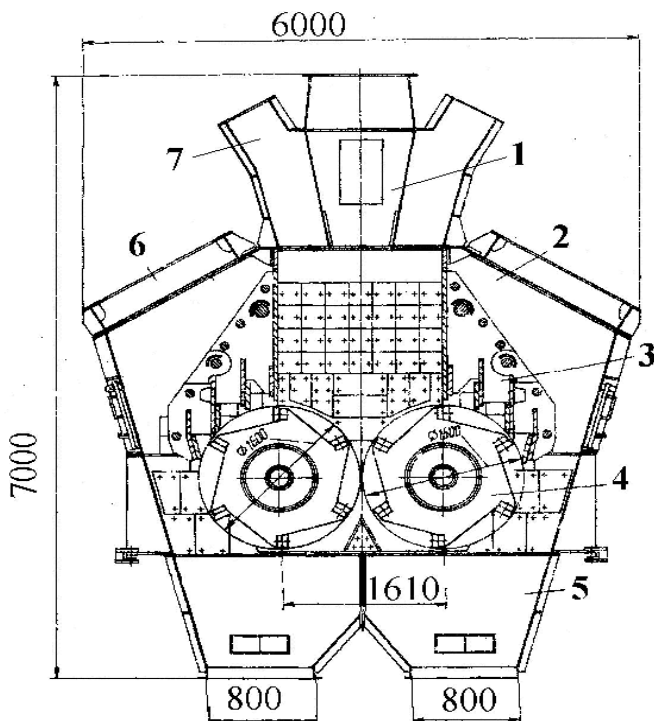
Двухроторная дробилка-сушилка СМД-209
